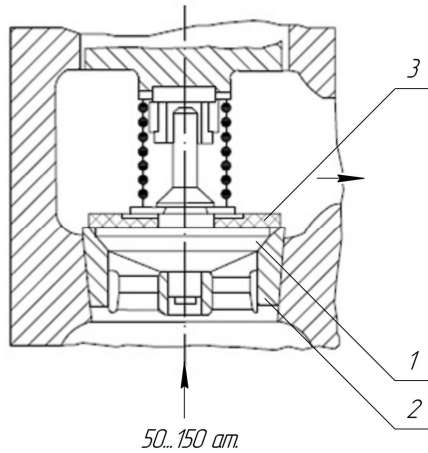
Конструкция клапана геологоразведочного грязевого насоса: 1 – тарелка клапана; 2 – седло клапана; 3 – резиновая прокладка
